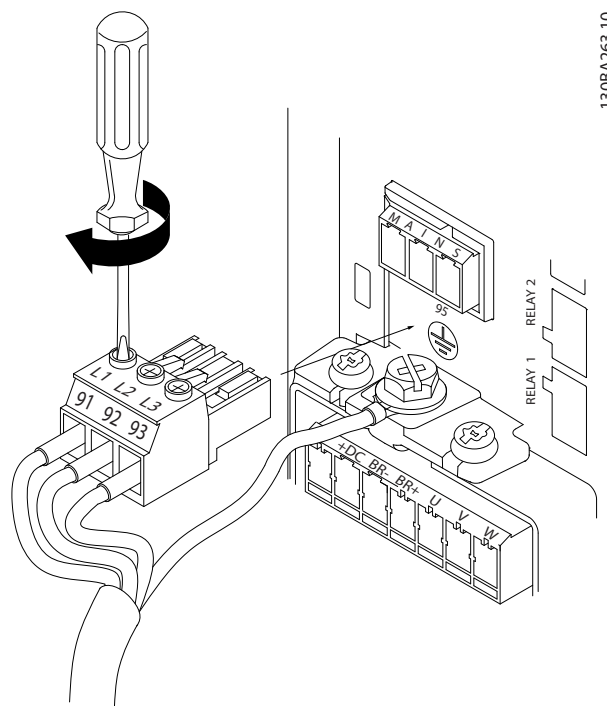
Montaje del conector de red y apriete de los cables
